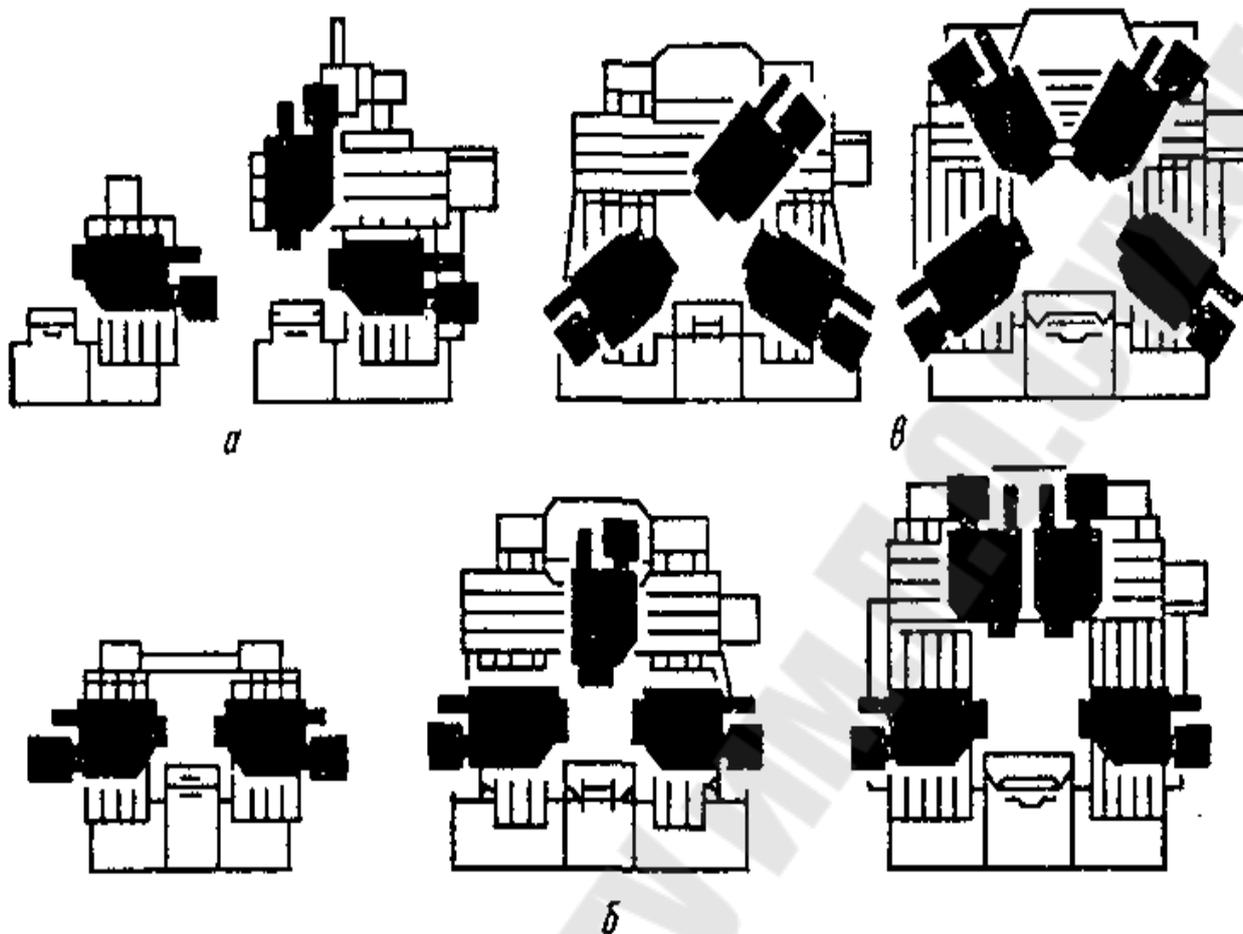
Схемы компоновок продольно-фрезерных станков:
